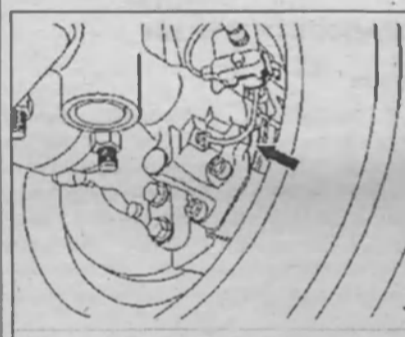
Проверка толщины тормозных накладок задних колес (автомобили с дисковыми тормозными механизмами).
